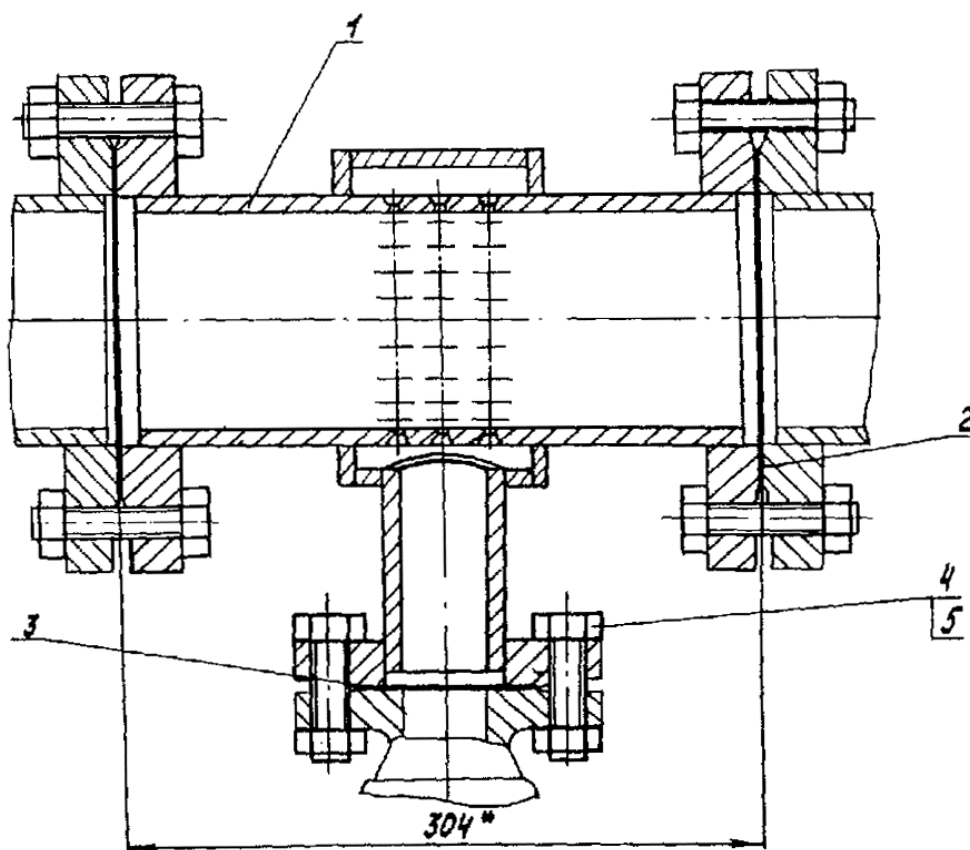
Распределительная головка для ввода ингибитора (сборочный чертеж):
